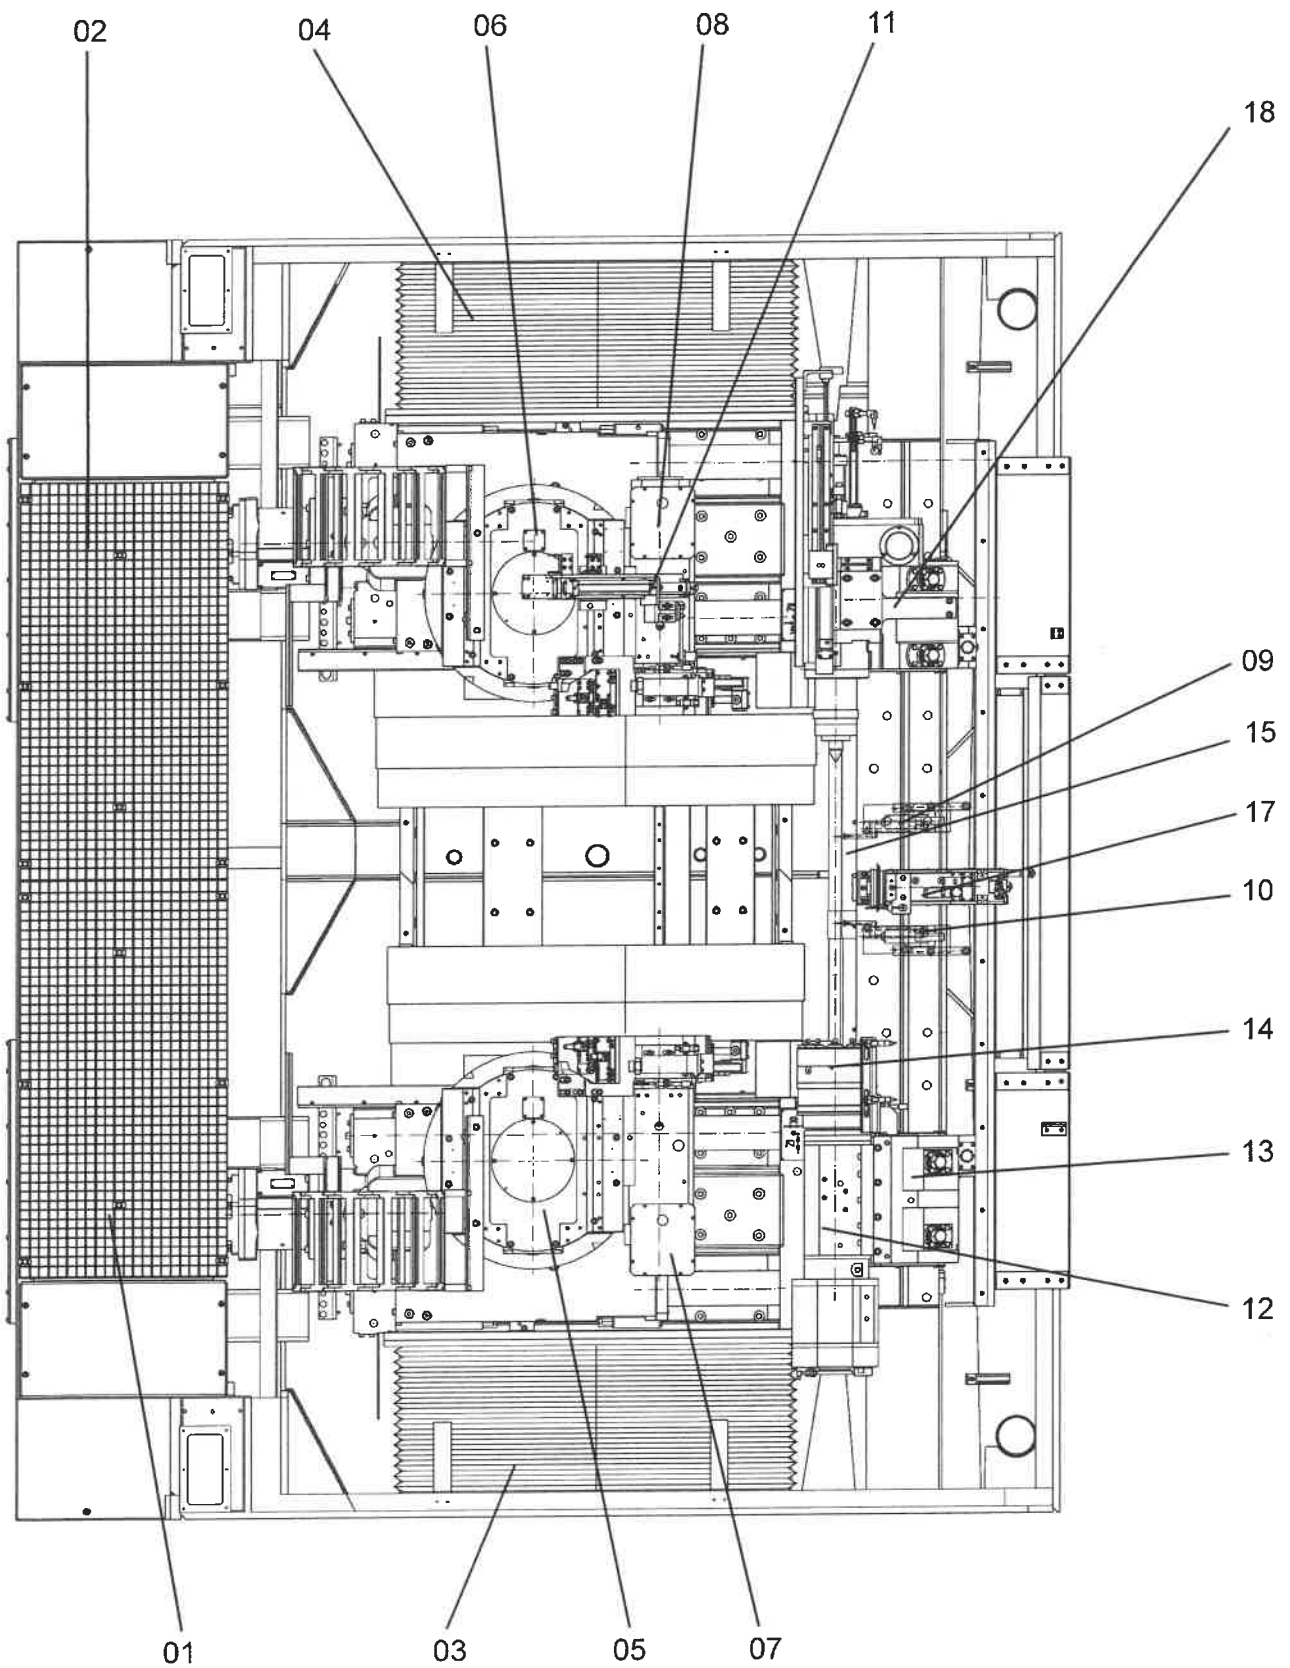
Draufsicht und Gesamtansicht (Innenraum Maschine)
